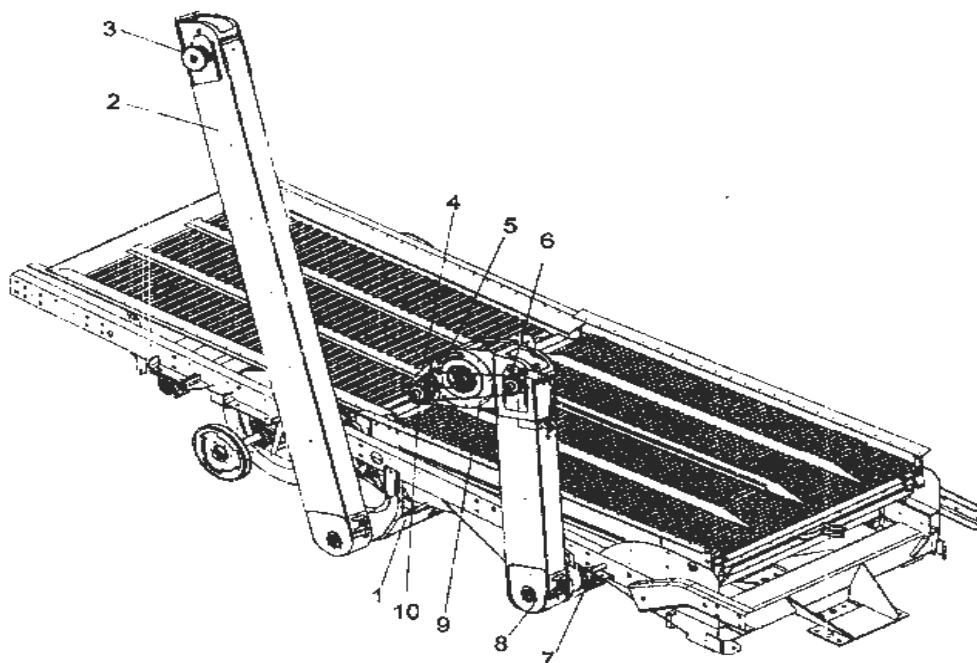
Транспортирующие устройства молотилки: 1 – шнек зерновой; 2 – элеватор зерновой; 3 – звездочка привода зернового элеватора; 4 – устройство домолачивающее; 5 – ролик натяжной; 6 – звездочка; 7 – шнек колосовой; 8 – элеватор колосовой; 9 – цепь; 10 – звездочка привода распределительного шнека домолачивающего устройства
